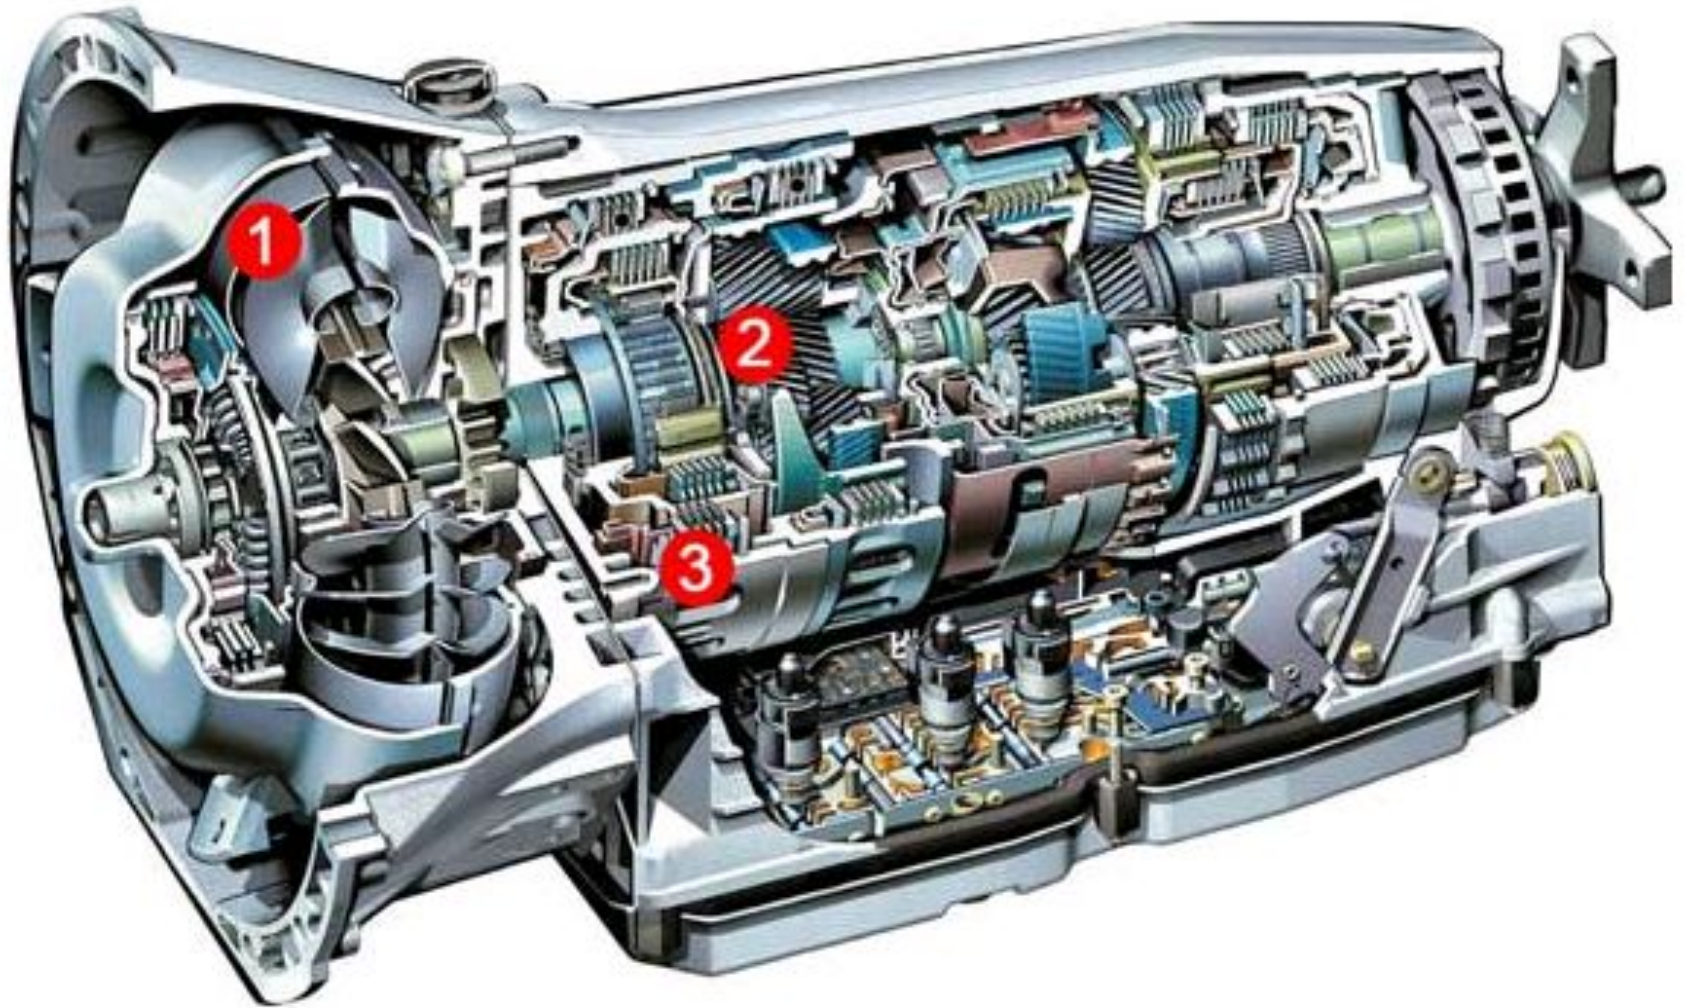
Автоматическая коробка передач: 1 – гидротрансформатор; 2 – планетарный редуктор; 3 – сцепления-фрикционы
